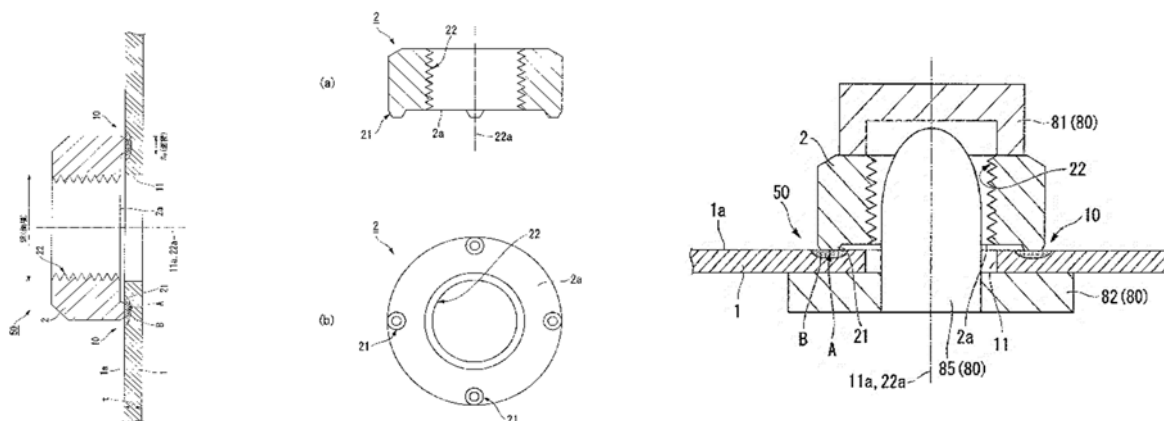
Способ рельефной сварки гайки с пластиной
